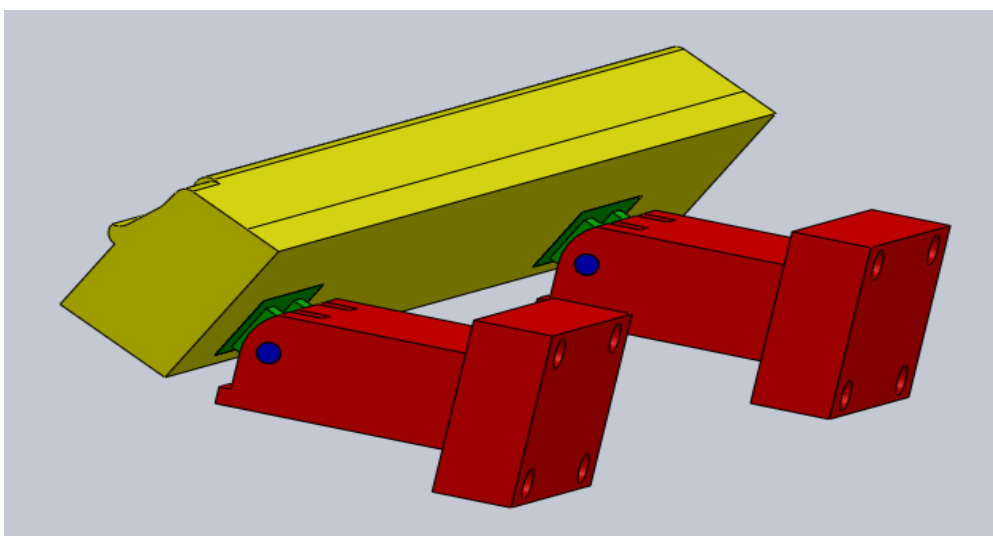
Porte pièce latérale conçue par Solidworks.
